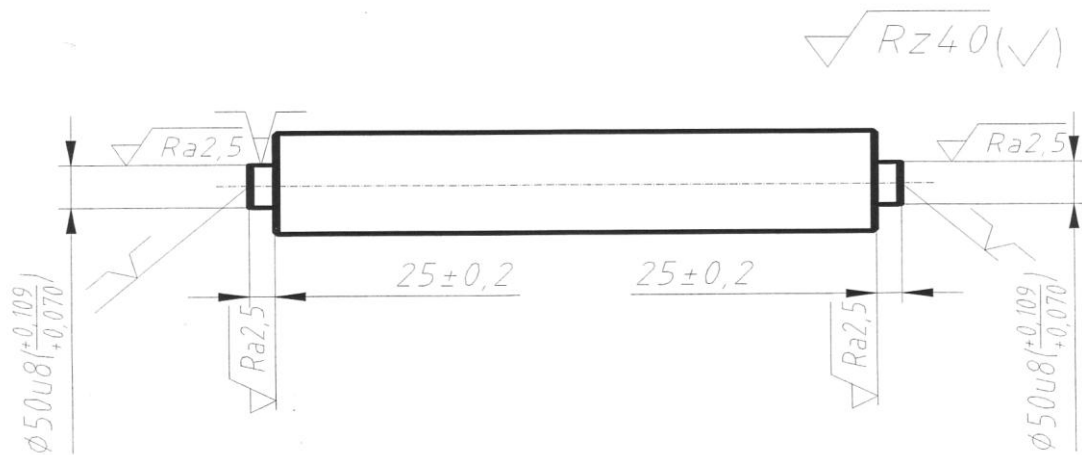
Ескіз обробки деталі операція №090
